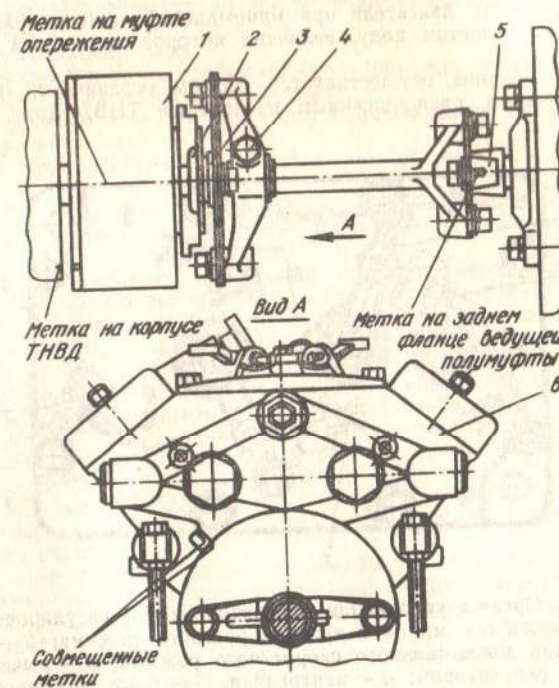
Установка ТНВД на двигатель КамАЗ-740 по меткам: 1 — автоматическая муфта опережения впрыска; 2 — ведомая полумуфта; 3 — фланец ведомой полумуфты; 4 — метка на корпусе ТНВД; 5 — задний фланец ведущей полумуфты; 6 — ТНВД
